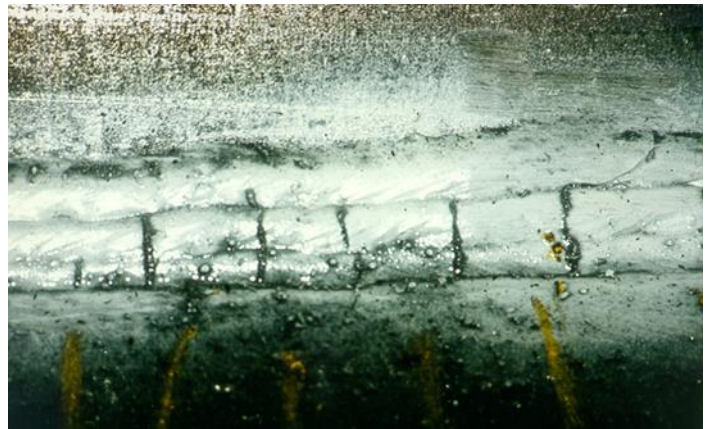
Kaltrisse in der zuletzt geschweißten Raupe
